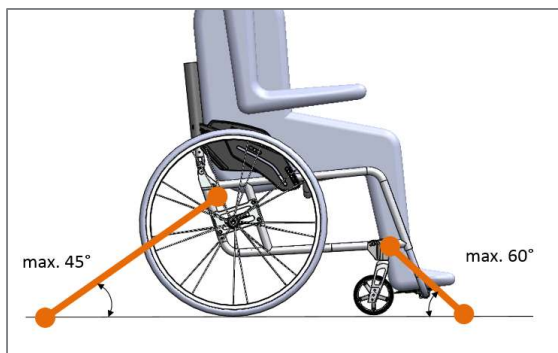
Andamento dei retrattori anteriormente e posteriormente con angolazione di ancoraggio massima e punti di collegamento (vista dal lato)
